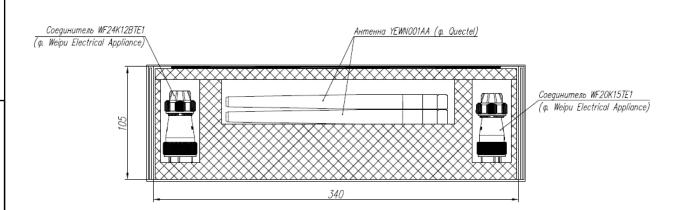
Габаритные размеры упаковки Изделия
